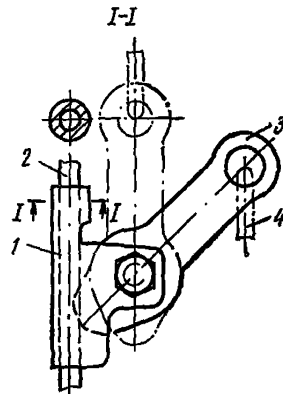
Ловитель для закрепления на страховочном тросе работающих с подвесной люльки
